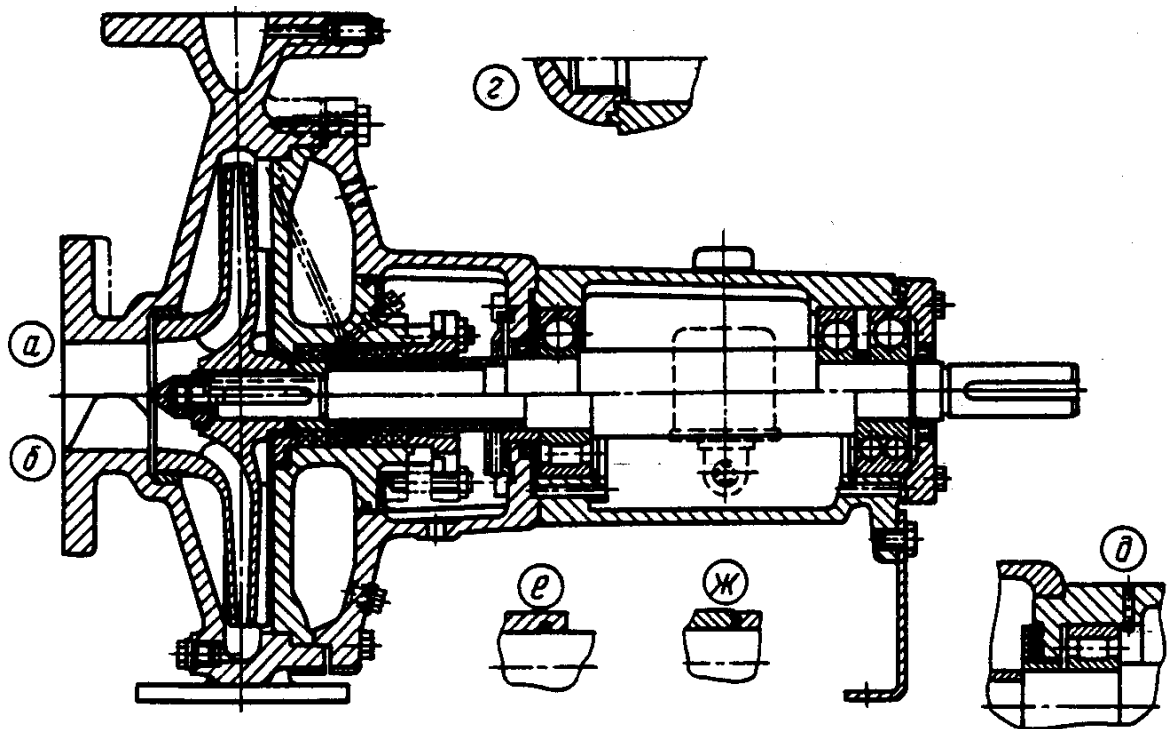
Элементы конструкций насосов с опорным корпусом.
